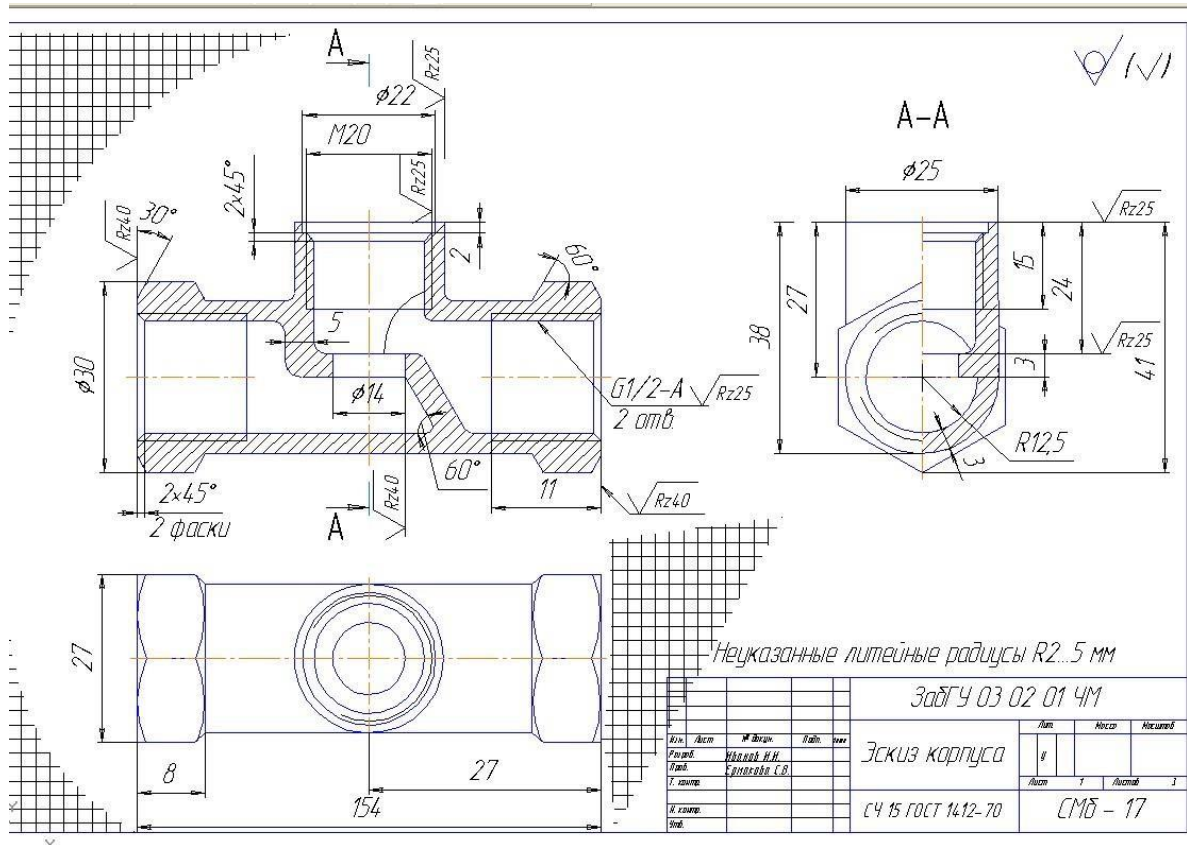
Образец выполнения задания «Эскиз корпуса»
